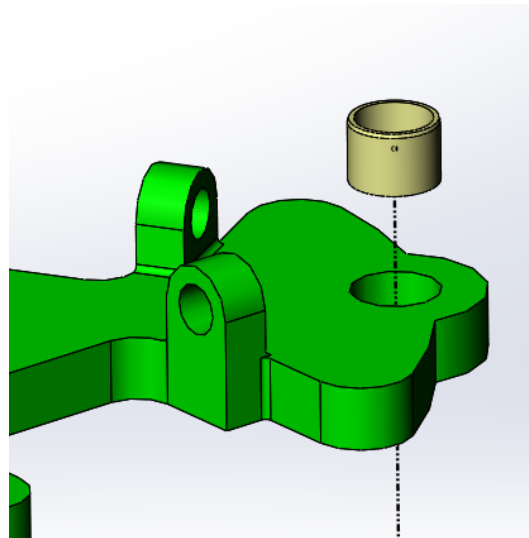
5ª parte da montagem - vista explodida da montagem.
